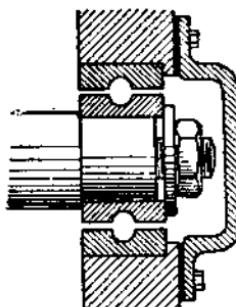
Посадка обоймы шарикоподшипника помо- щью прессовой посадки
